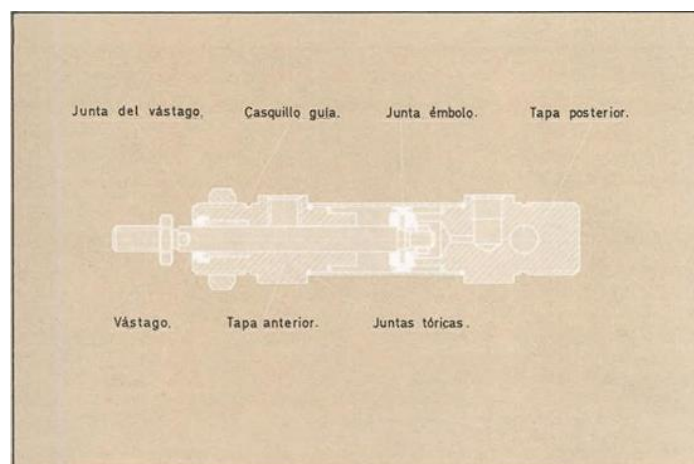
Cilindro neumático. Elementos principales de que consta.
